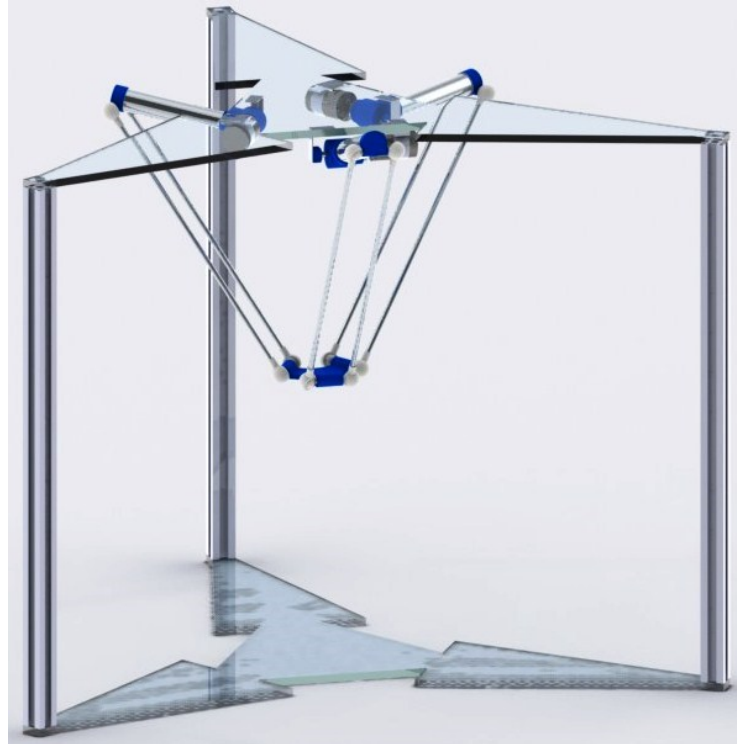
vista Isométrica del Robot Delta. Diseño propio elaborado en SolidWorks®
